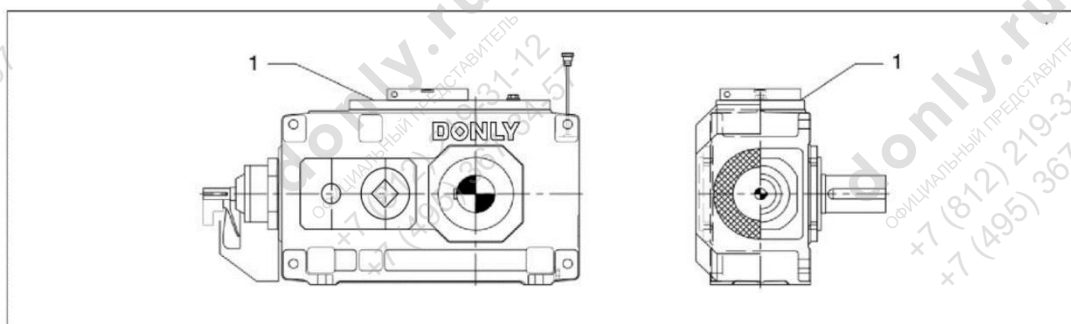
Центровочные поверхности на редукторах моделей 3–12
